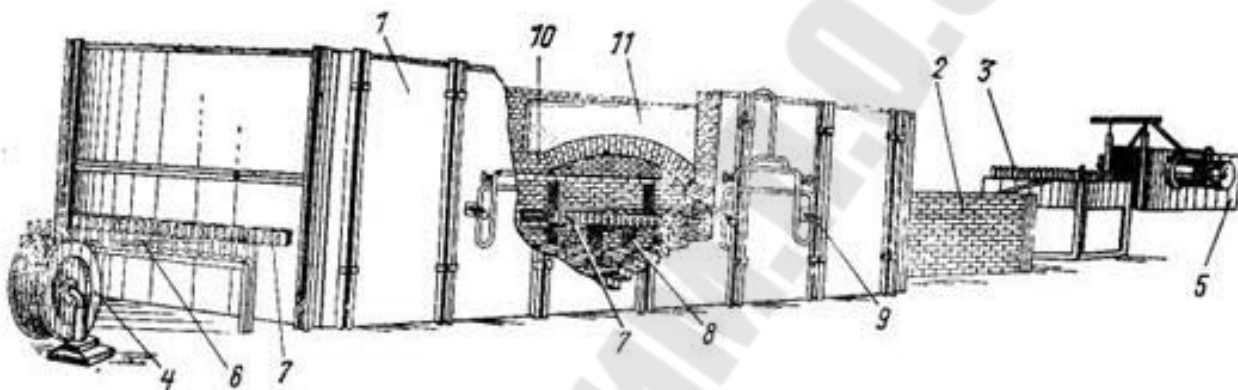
Патентировочный агрегат: 1 — нагревательная печь; 2 — ванна с расплавом соли (свинца); 3 — промывочная ванна; 4 — размоточная катушка; 5 — намоточный аппарат; 6 — обрабатываемая проволока; 7 — муфели; 8 — подставки для муфелей; 9 — горелка или форсунка; 10 — огнеупорная кладка; 11 — теплоизоляционная засыпка.
